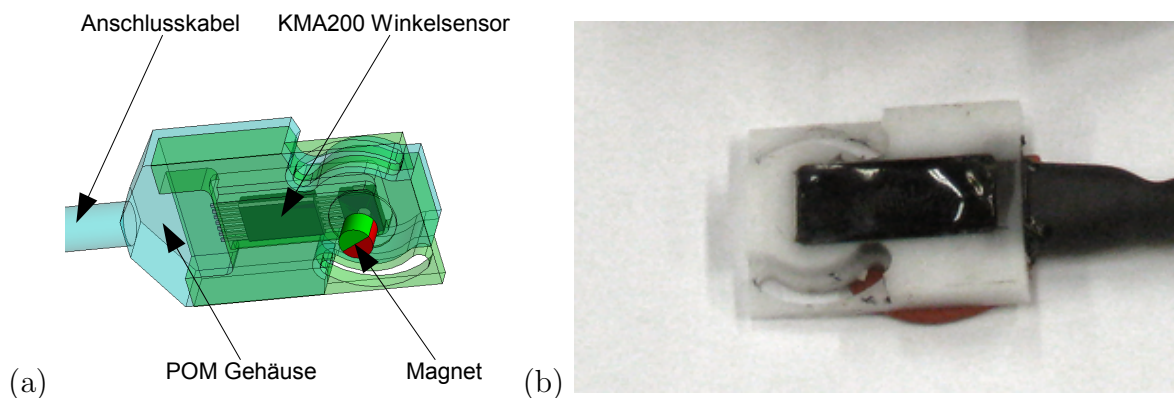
CAD Ansicht (a) des druckneutralen Winkelsensors (b)
